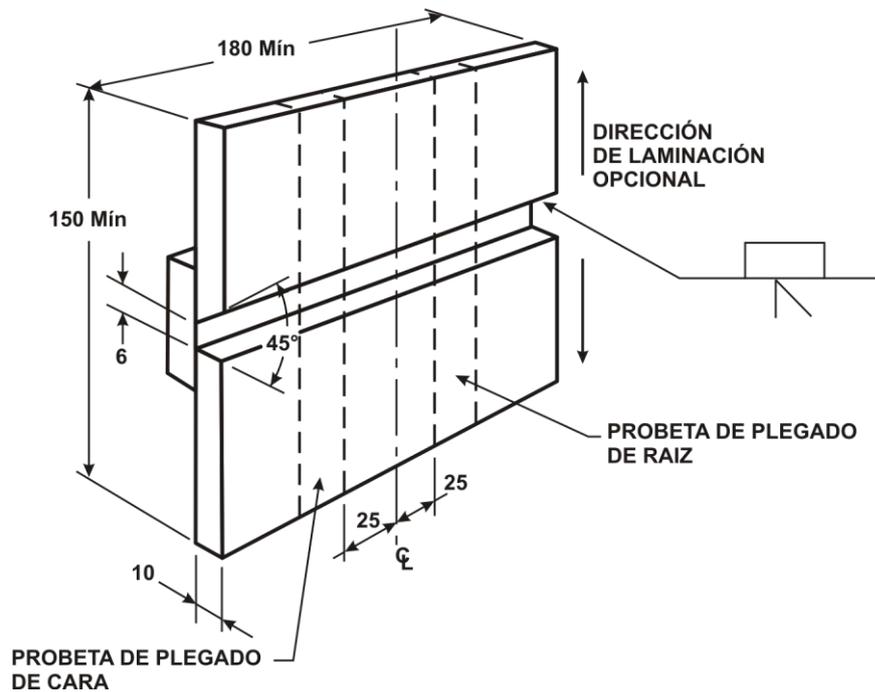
Chapa de ensayo opcional para espesor ilimitado – Posición horizontal – Calificación de soldador.
